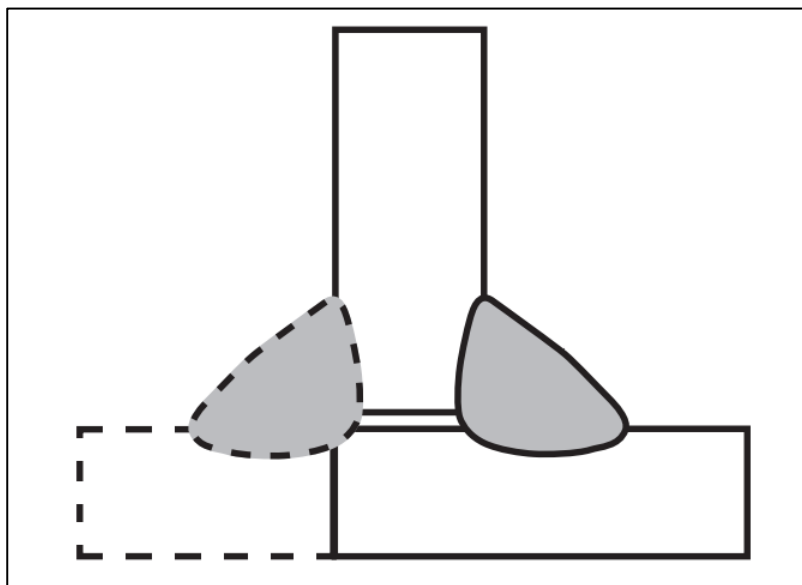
Ejemplo De Soldadura De Filete En Junta Con Penetración Parcial (PJP) [58].
